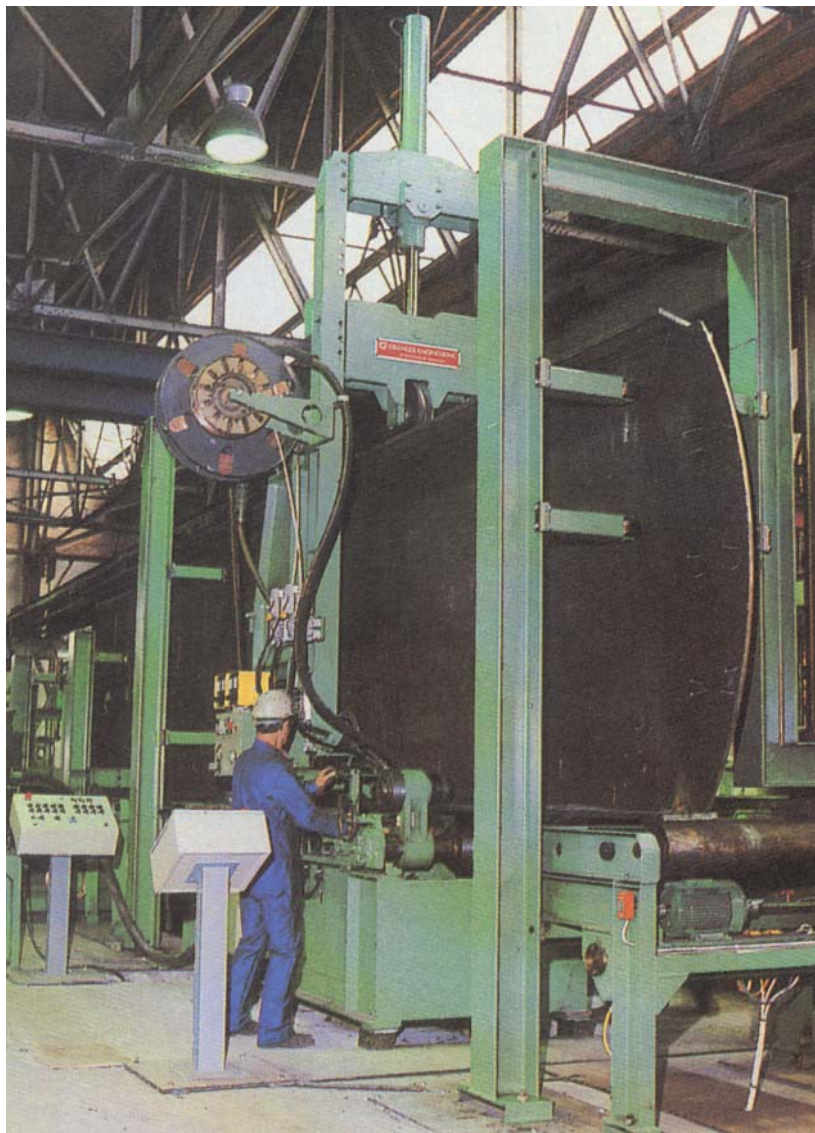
Armado y soldadura de vigas en horizontal o en vertical.
